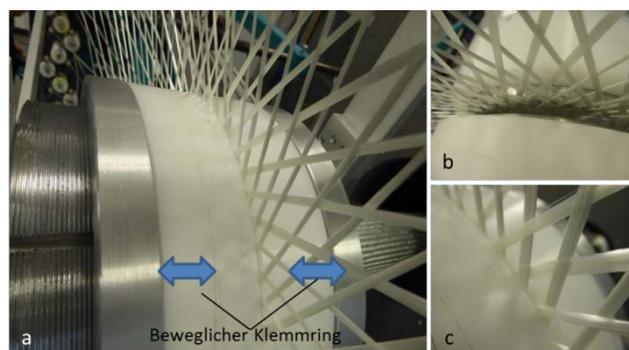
Schema des Flecht-Klemmringes (a) und Detailaufnahmen vom geöffneten Zustand zum Flechten (b) und vom geschlossenen Zustand zum Klemmen (c)
